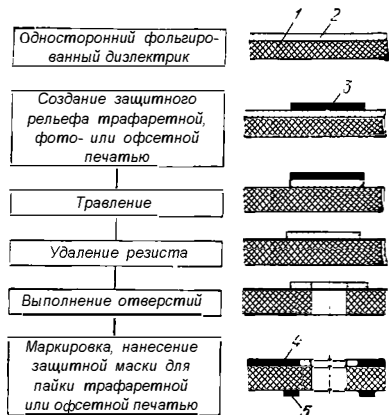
Схема технологического процесса изготовления ОПП: 1 — материал основания; 2 — фольга; 3 — фоторезист; 4 — защитная маска; 5 — маркировка
